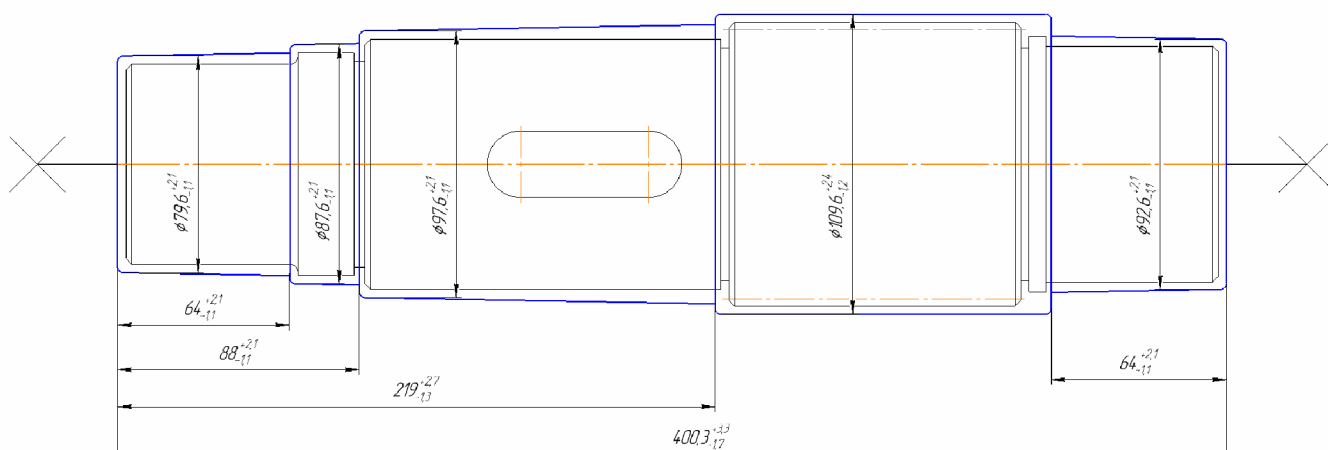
Ескіз заготовки, що виготовлена ковкою на ГКМ
